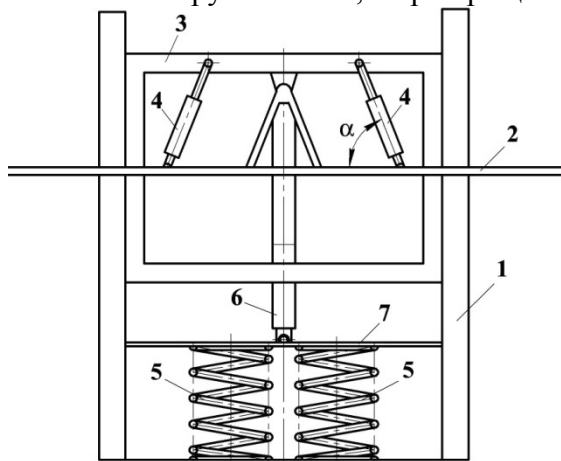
Схема к расчету вертикальных пружин: 1 – вертикальные направляющие рамы опрыскивателя; 2 – штанга; 3 – подвижная рамка; 4 – амортизаторы; 5 – вертикальные упругие элементы (пружины); 6 – гидроцилиндр изменения высоты установки штанги; 7 – пластина
